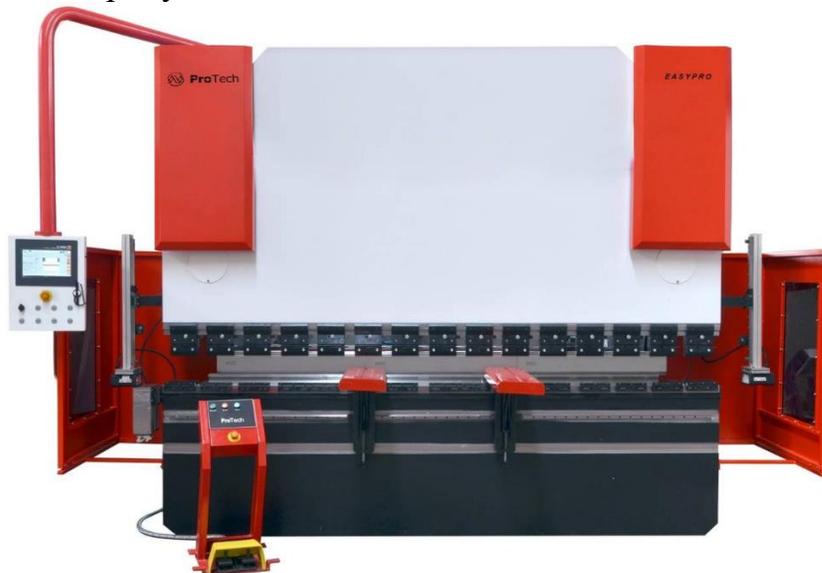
Гидравлический гибочный пресс ProTech EASYPRO 3700-220
